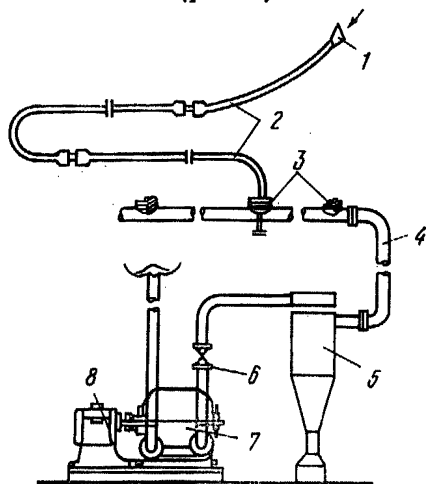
Схема высоковакуумной установки для местного отсоса пыли и газов от сварочной дуги:
